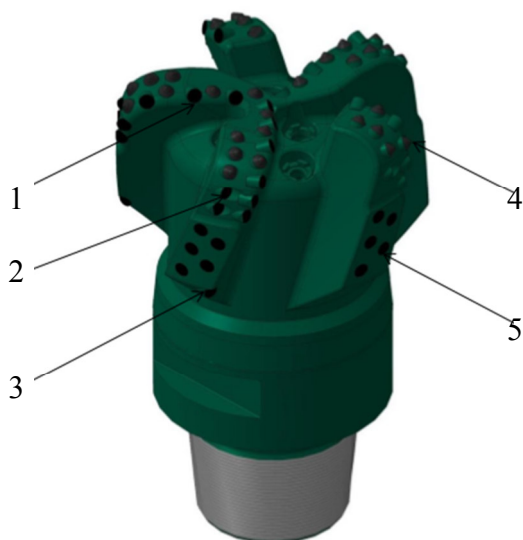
Долото «Булава» компании «БУРСЕРВИС»: 1 – стандартные резцы PDC; 2 – двойной ряд резцов PDC на калибрующей части лопасти долота; 3 – резцы обратной проработки; 4 – резцы конической формы; 5 – резцы PDC на калибрующей поверхности
